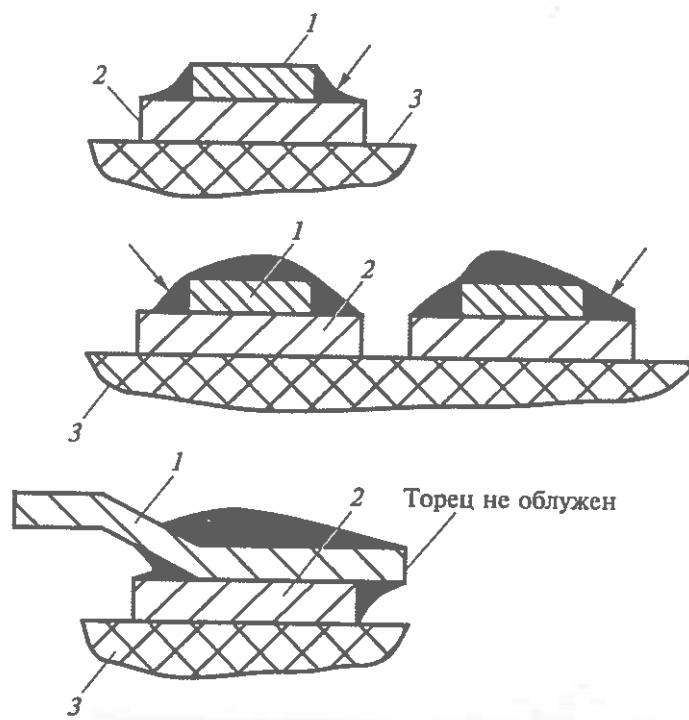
Рекомендуемые формы паянных соединений планарных выводов ИМС с контактными площадками печатных плат:
